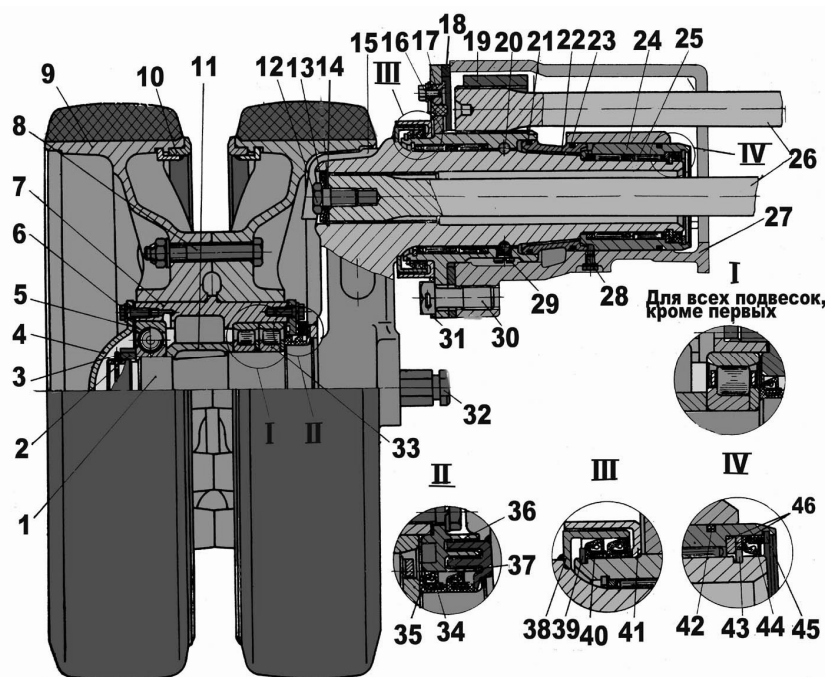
Опорный каток с элементами подвески: 1 – балансир; 2 – гайка; 3 – шплинт; 4, 13 – крышки; 5 – шарикоподшипник; 6, 8, 12 16, 30 – болты; 7 – ступица; 9 – диск; 10 – реборда; 11 – распорная втулка; 14 – пружинные кольца; 15 – скребок; 17 – заглушка; 18 – регулировочная прокладка; 19 – втулка; 20 – шарик; 21, 23 – уплотнительные кольца; 22 – распорная втулка; 24 – обойма подшипника; 25 – игольчатый подшипник; 26 – торсионные валы; 27 – кронштейн; 28, 29 – пробки; 31 – стопорная шайба; 32 – палец; 33 – роликовый подшипник; 34 – пластинчатая пружина; 35, 40, 44 – манжеты; 36 – крышка лабиринтного уплотнения; 37, 38, 41 – лабиринтные кольца; 43 – проставочное кольцо; 46 – сектор
